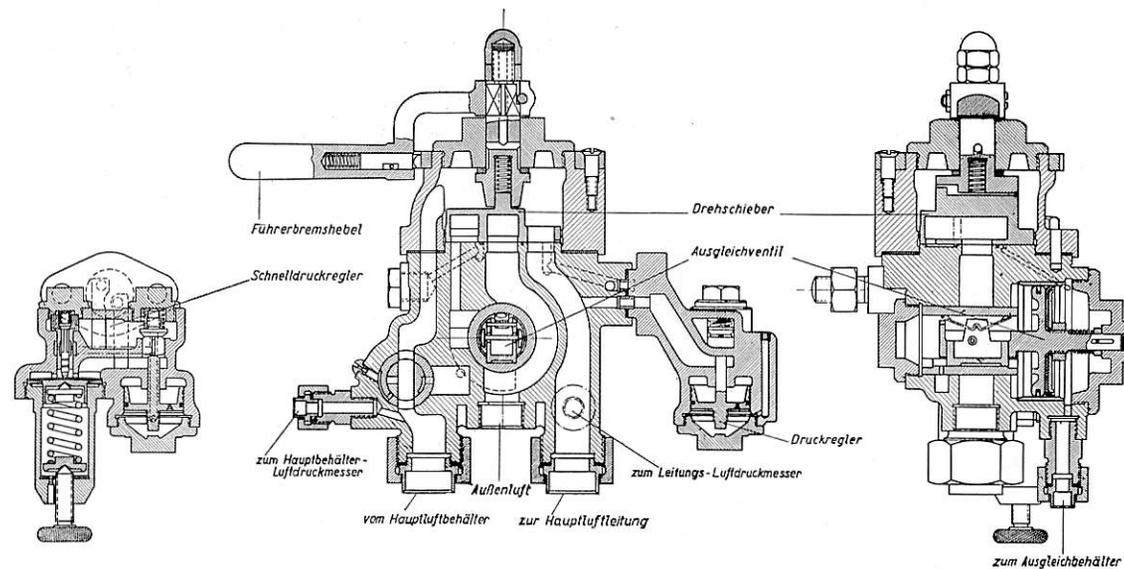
Knorr-Drehschieberführerbremsventil mit Schnelldruckregler und Ausgleichventil.
